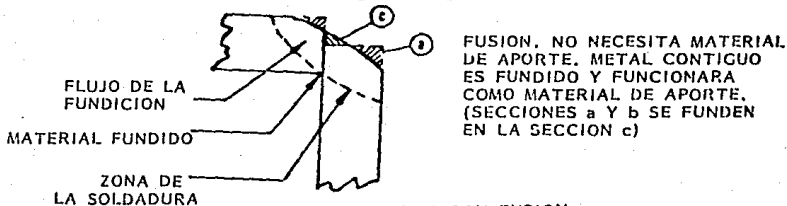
SOLDADURA CON FUSION
